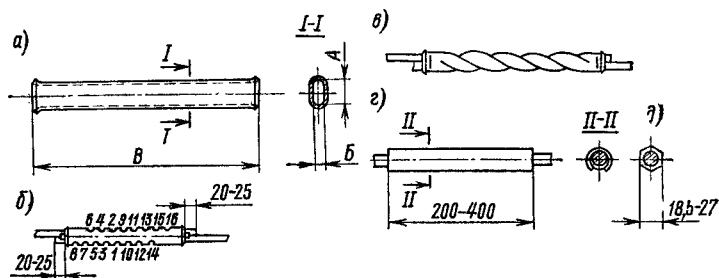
Овальные соединители и ремонтные зажимы: а — овальный соединитель типа САО или СОАС; б — обжатие овального соединителя на сталеалюминиевом проводе АС-70 + АС-185; в — овальный соединитель, смонтированный скручиванием; г — ремонтный зажим типа РАС для проводов сечением $95-185 \text{ мм}^2$; д — сечение ремонтного зажима, опрессованного шестигранной матрицей
